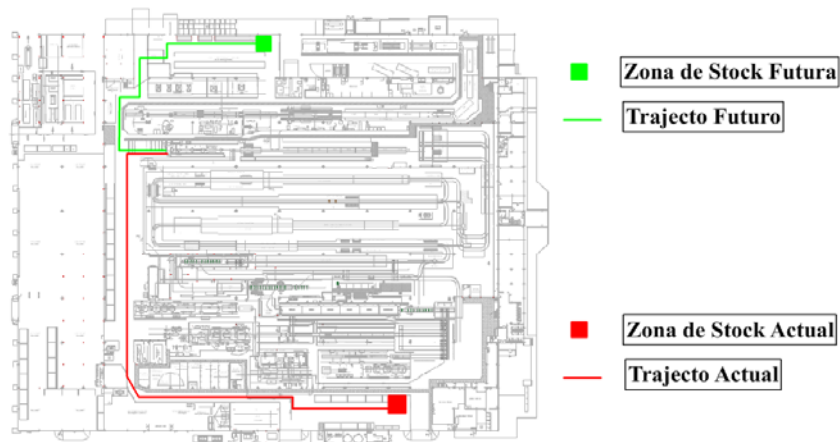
Layout com trajectos e zonas de stock actuais e futuras
